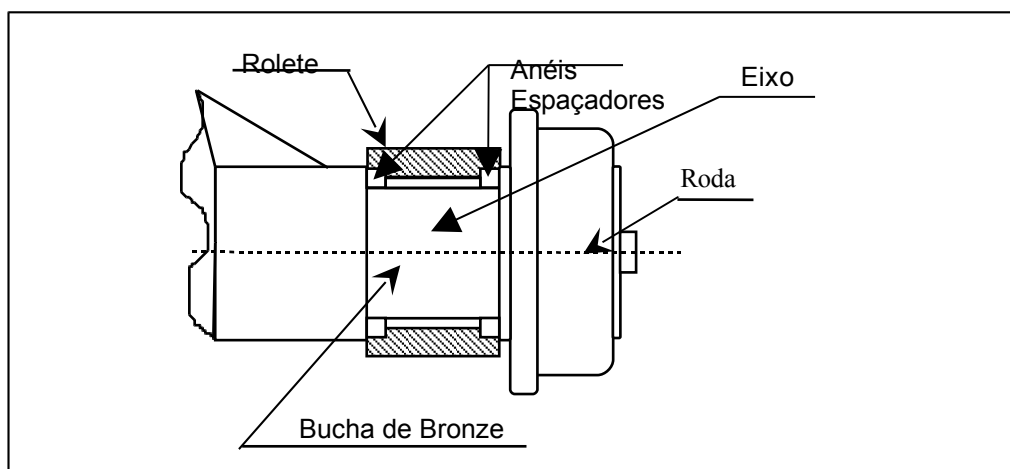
Detalhes do conjunto original de eixo das caixas de Sinter.
